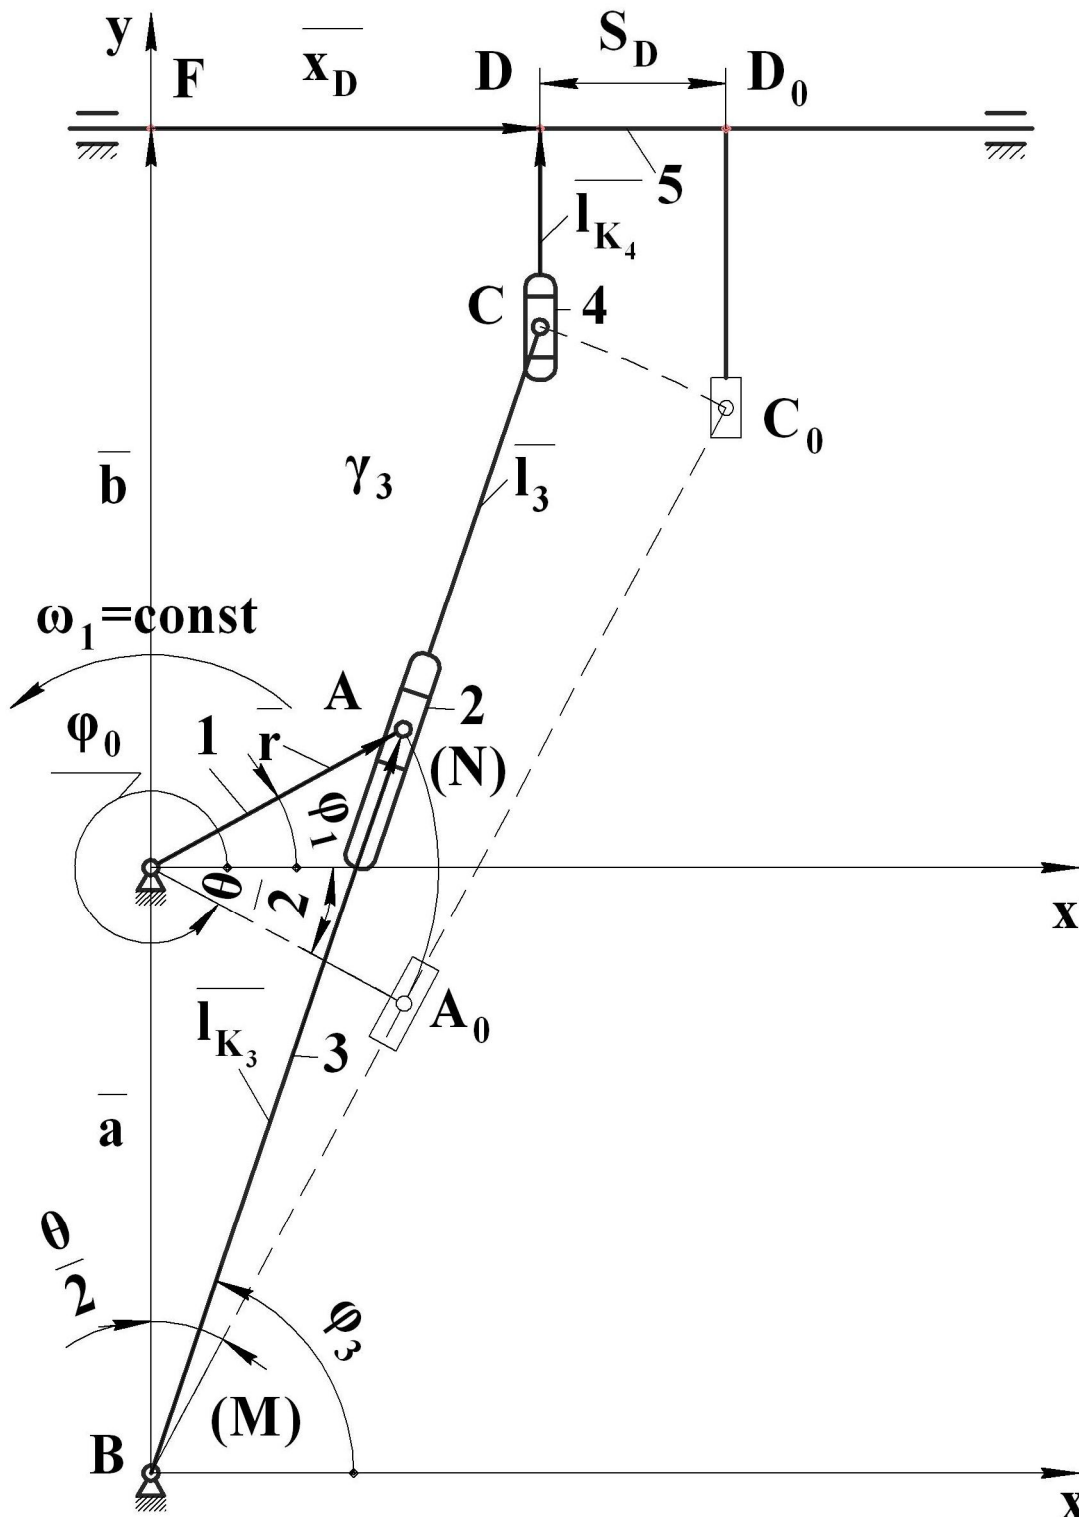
Шестиланковий кулісний механізм поперечно-стругального верстата
